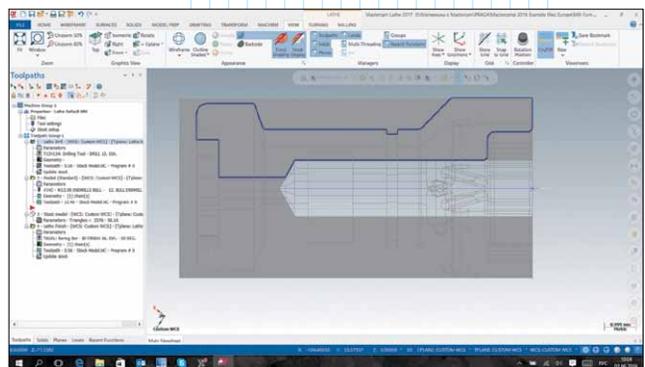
Пример осевого сверления детали в токарном модуле Mastercam
